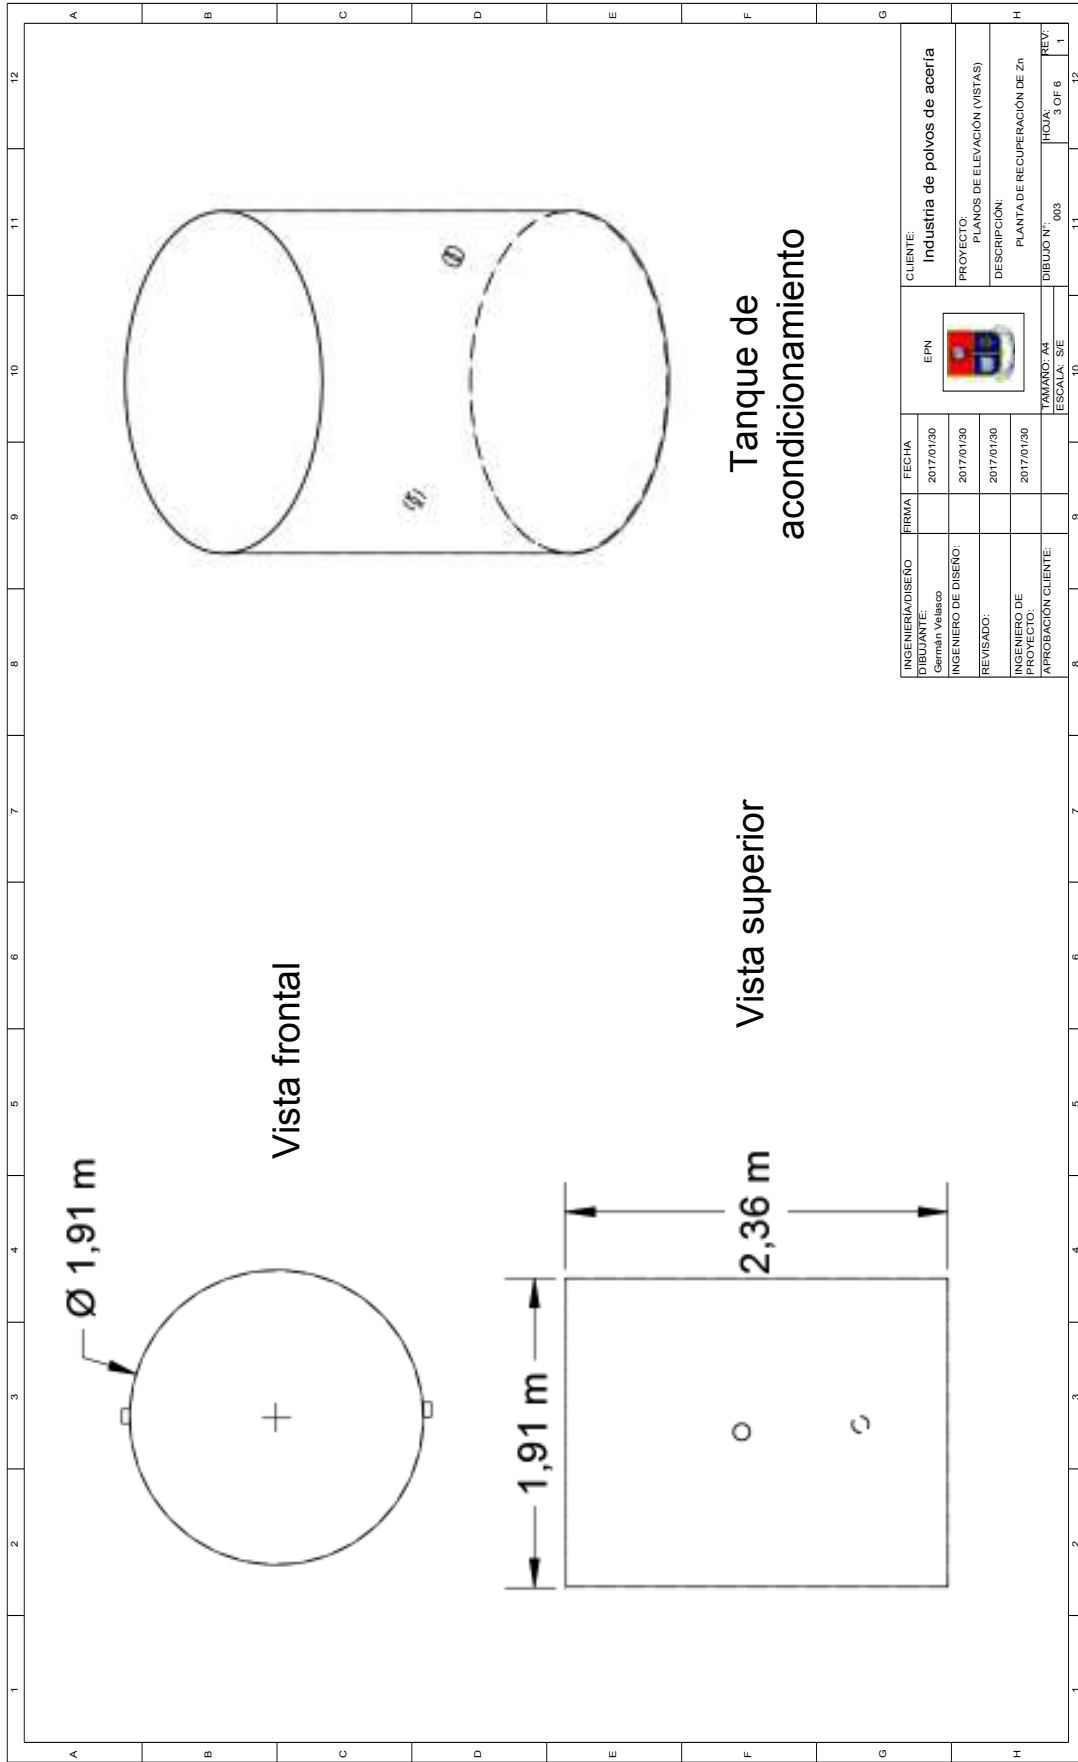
Plano de elevación del tanque de acondicionamiento de pH
